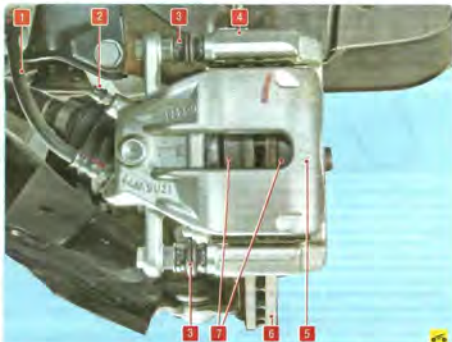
Тормозной механизм переднего колеса: 1 – тормозной шланг; 2 – клапан выпуска воздуха; 3 – направляющий палец суппорта (закрит защитным чехлом); 4 – направляющая колодок; 5 – суппорт тормозного механизма; 6 – тормозной диск; 7 – тормозные колодки
